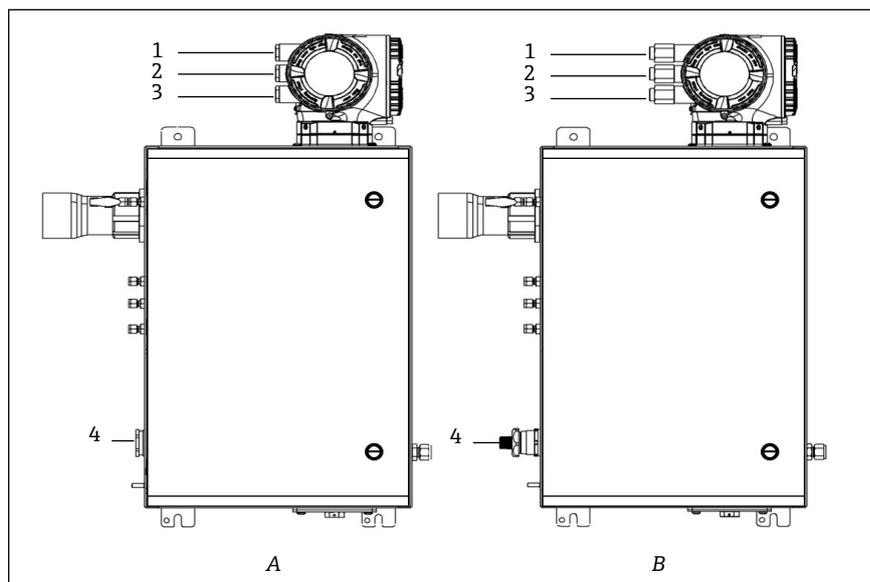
Gewindeeinführungen für J22-Gehäuse für ATEX- (A) und zöllige (B) Anschlüsse
